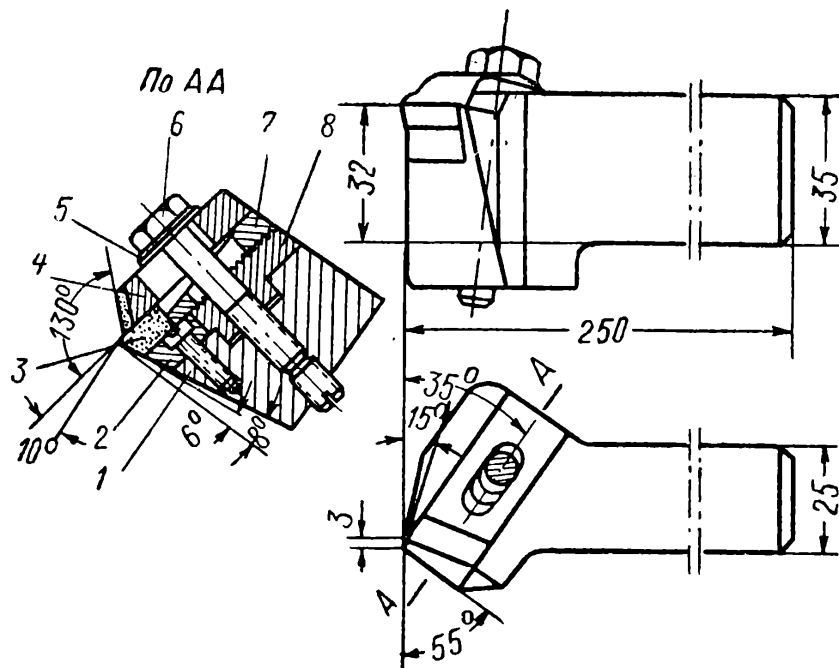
Резец с механическим креплением пластинок твердого сплава конструкции Цниитмаш:
